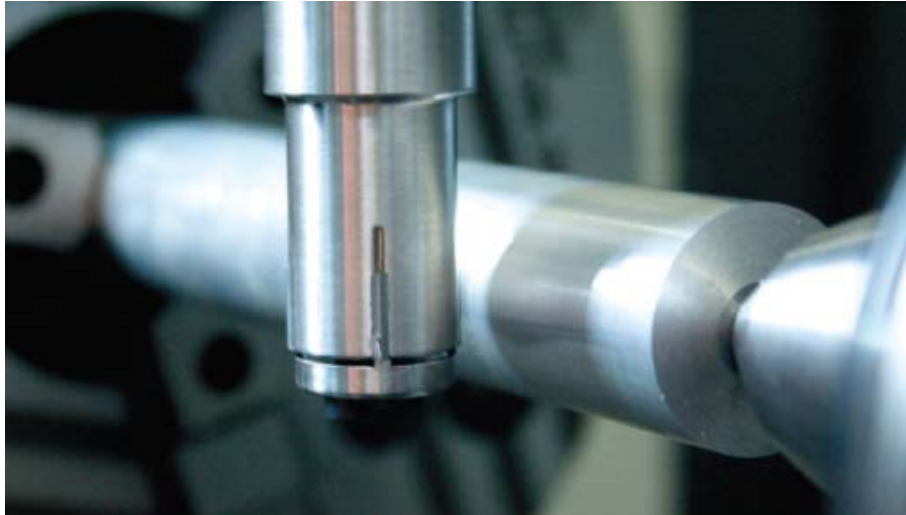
Werkzeug und Werkstück vor der Bearbeitung
